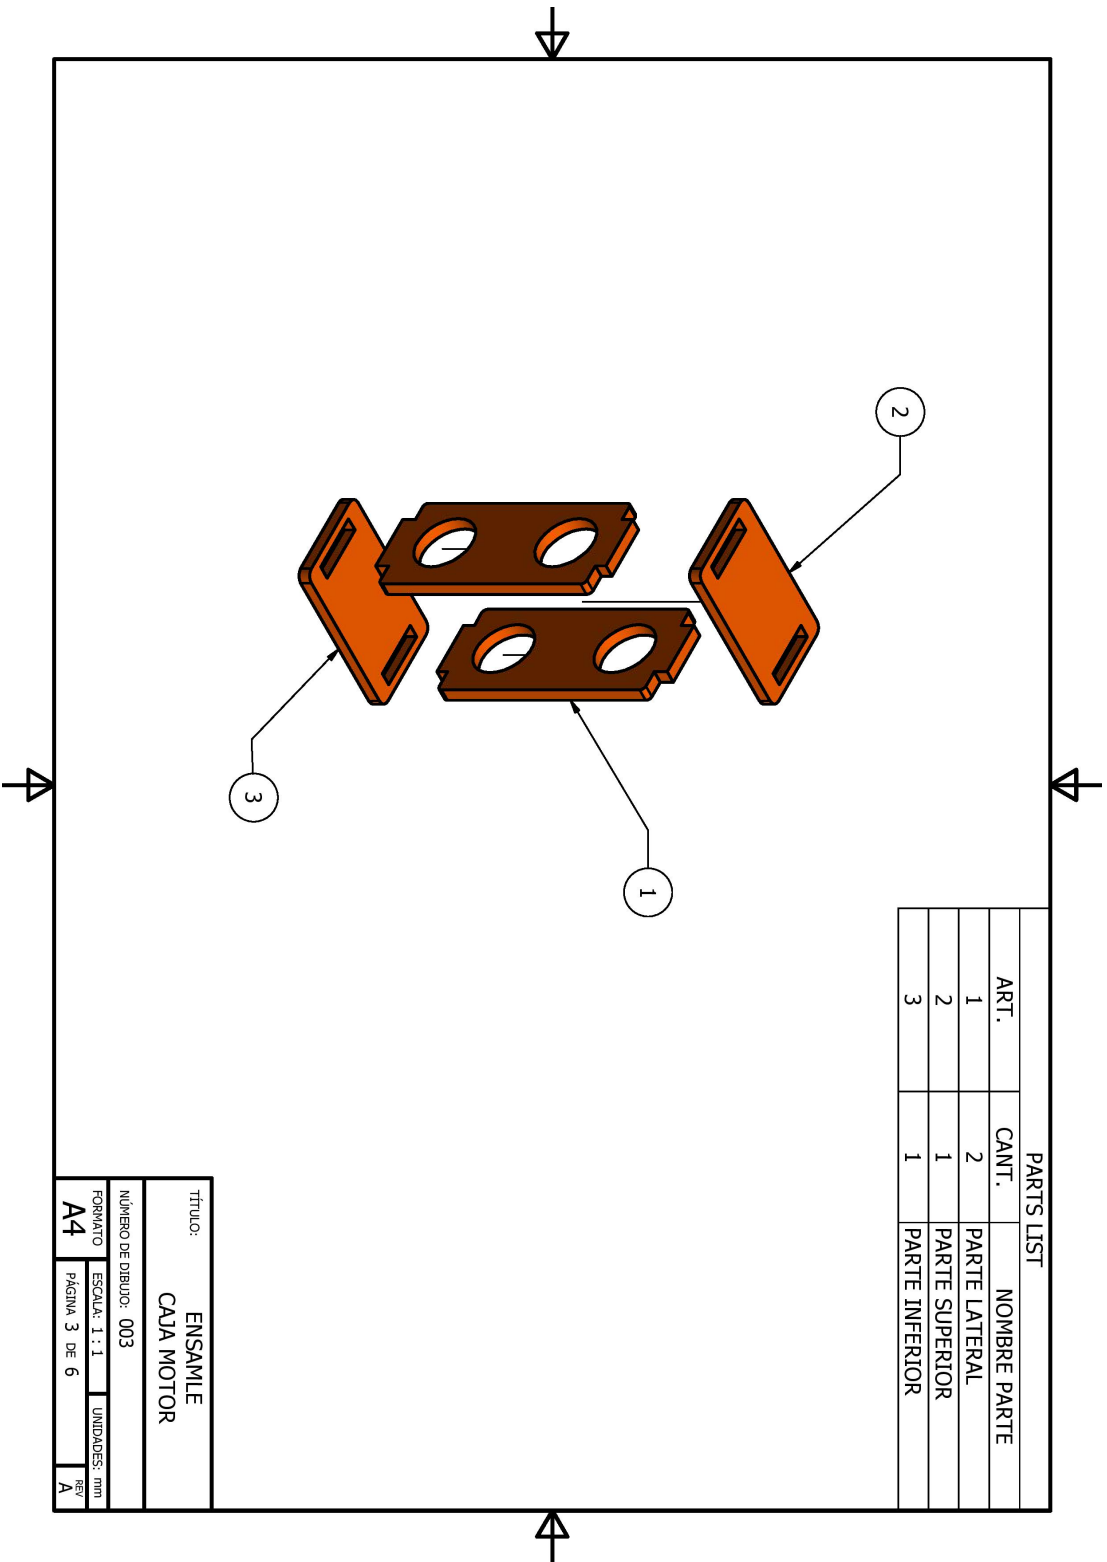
Plano de explosión de ensamble de caja para acople de motor a base
